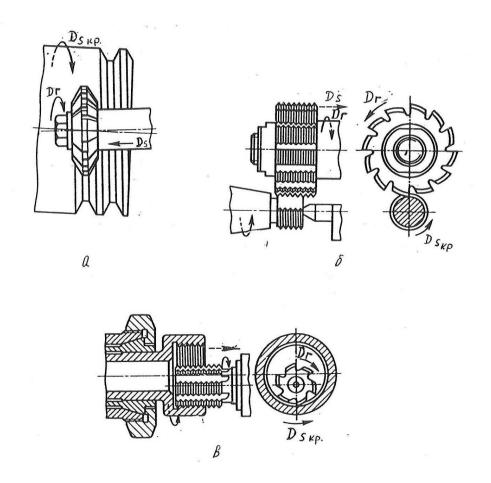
Схемы резьбонарезания на фрезерном станке: а — резьбофрезерование дисковой фрезой; б — резьбофрезерование гребенчатой фрезой наружной поверхности; в — резьбофрезерование гребенчатой фрезой внутри отверстия
